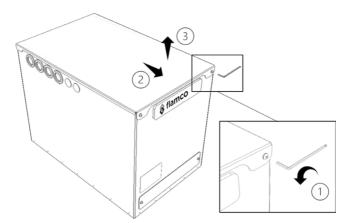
Retrait du couvercle de la batterie de chauffage Flextherm Eco G2 D
